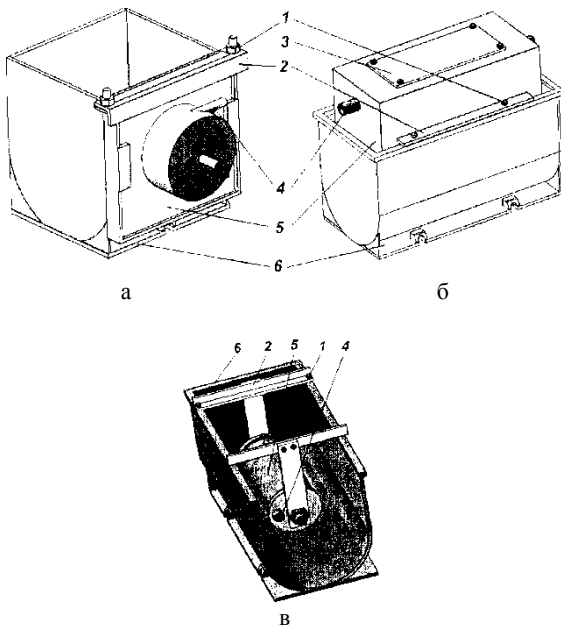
Конструкций рабочих контейнеров с различными схемами расположения ультразвукового преобразователя:
